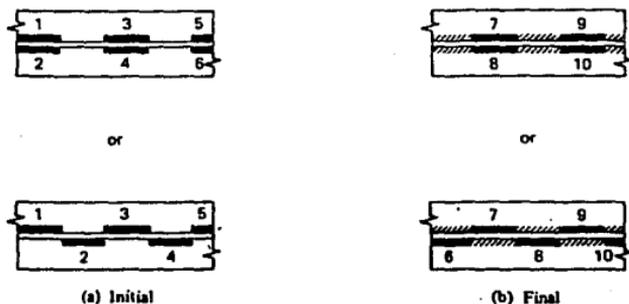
Secuencia para soldaduras intermitentes.
